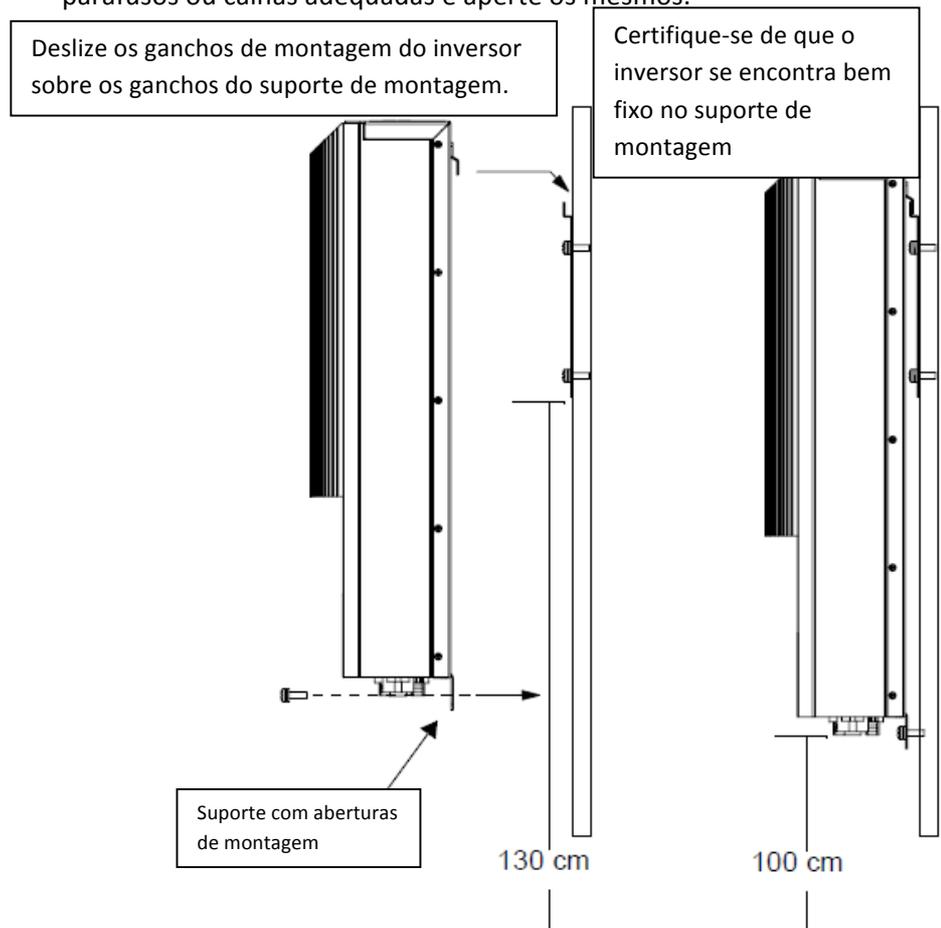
Colocação Correcta do Inversor no Suporte de Montagem
